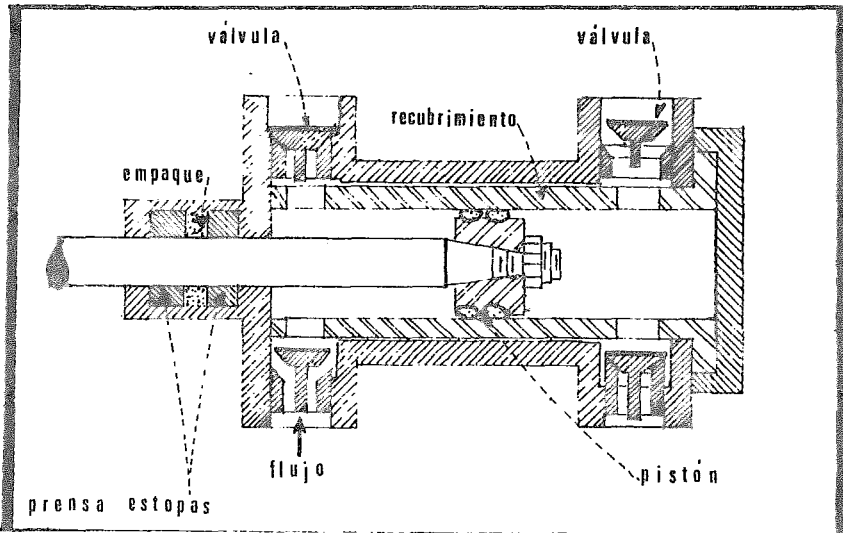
DIBUJO ESQUEMATICO DE UNA BOMBA DE PISTON DUPLEX.
